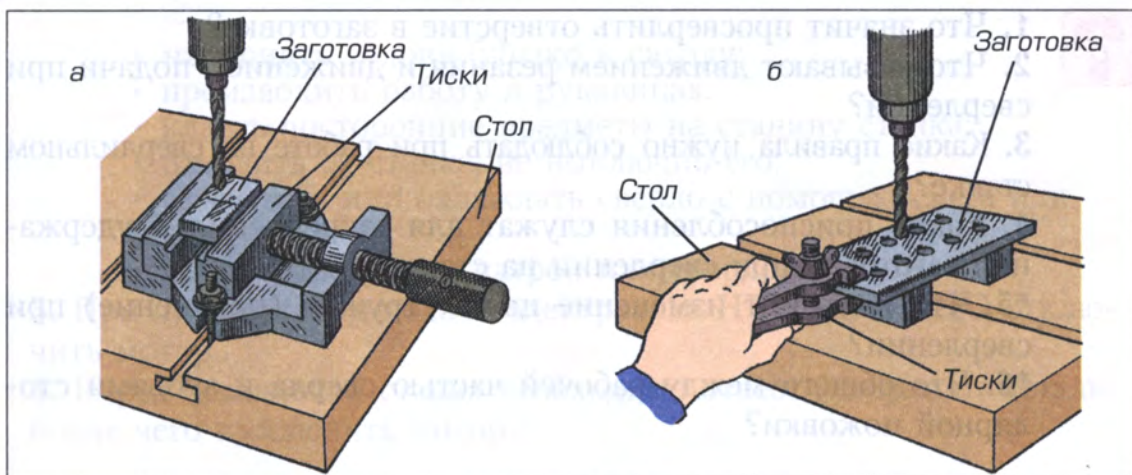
Машинные (а) и ручные (б) тиски для закрепления заготовок при сверлении на станке
